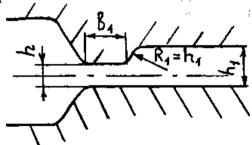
Форма заусенечной канавки для прессовых штампов
